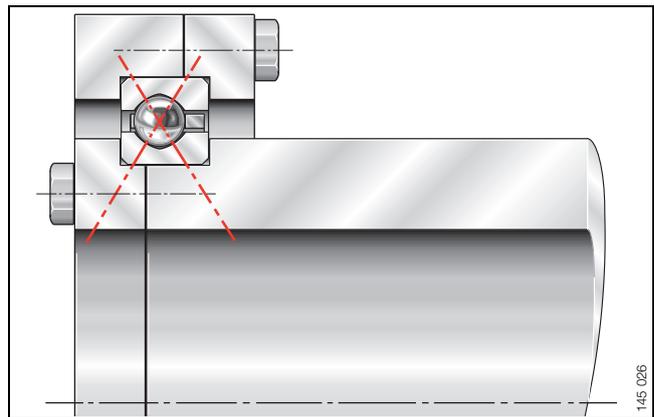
· Vierpunktlager – Konstruktionsbeispiel
